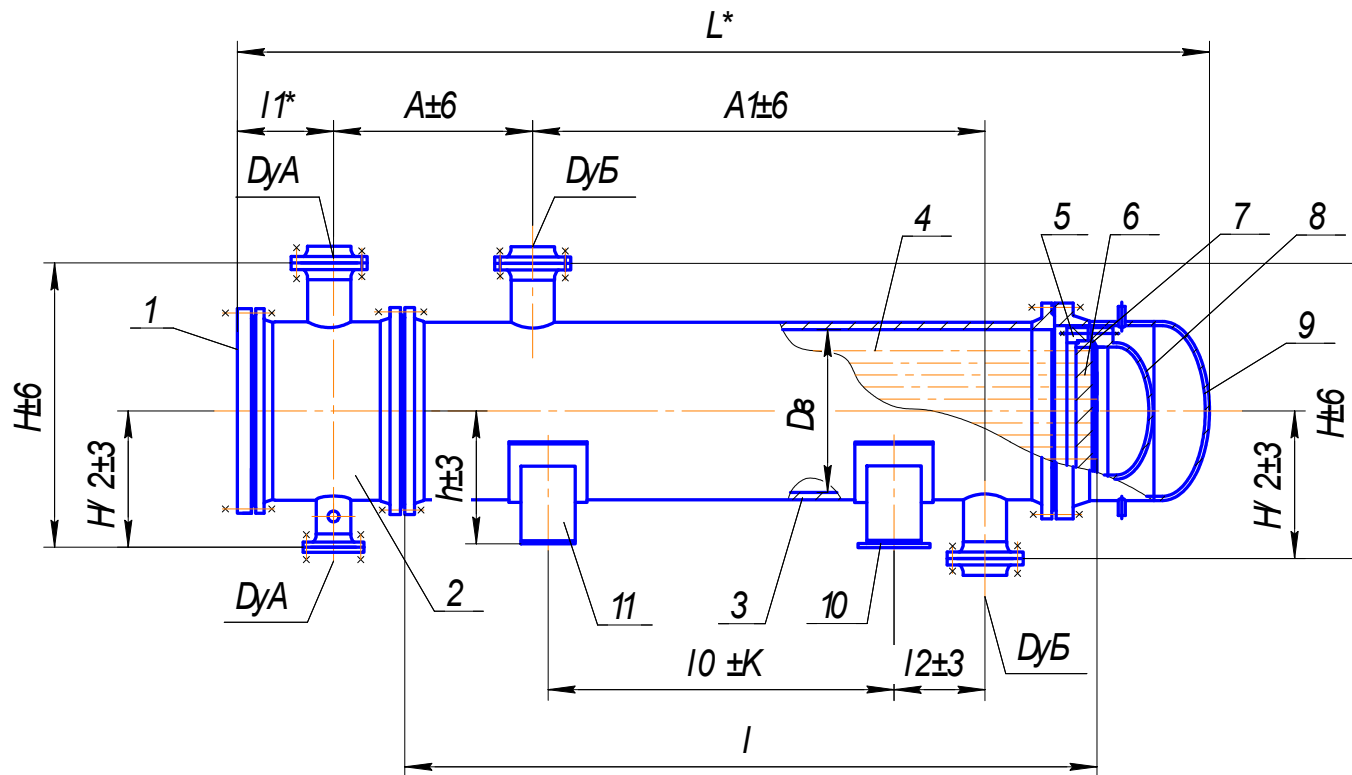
Аппарат типа XIII. 1 – крышка камеры распределительной; 2 – камера распределительная; 3 – кожух; 4 – труба теплообменная; 5 – полукольцо; 6 – решетка трубная подвижная; 7 – прокладка плавающей головки; 8 – крышка плавающей головки; 9 – крышка кожуха; 10 – опора подвижная; 11 – опора неподвижная.
